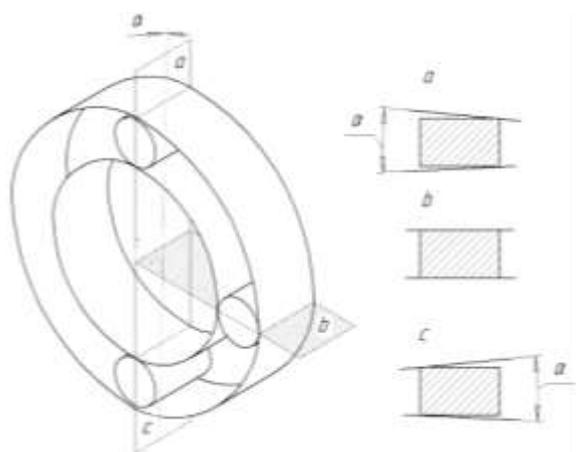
Схема взаимного расположения ролика и поверхностей колец подшипника
